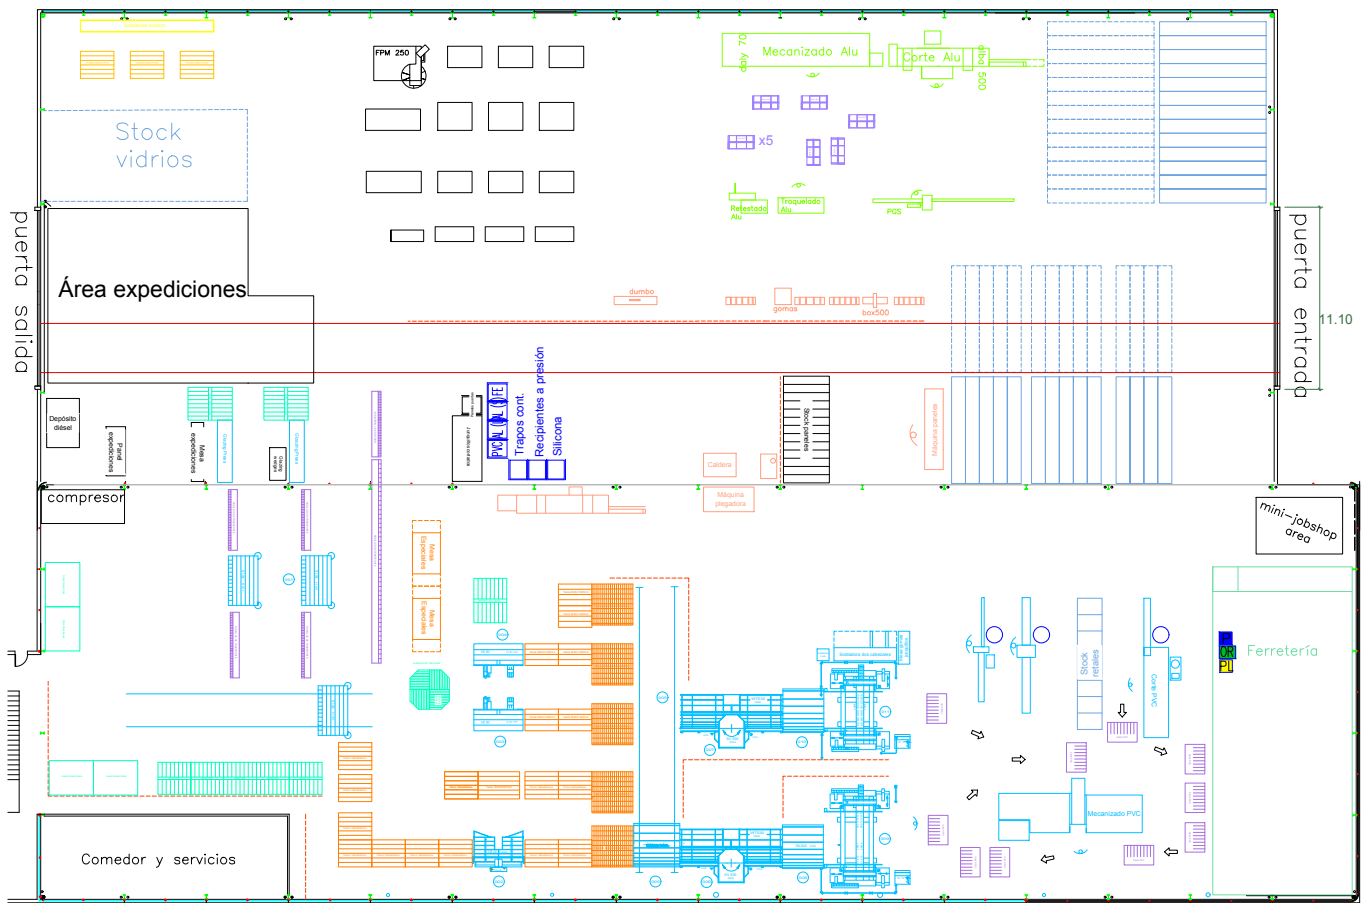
Alternativa 3 de la distribución en planta (Fuente: Elaboración propia)
